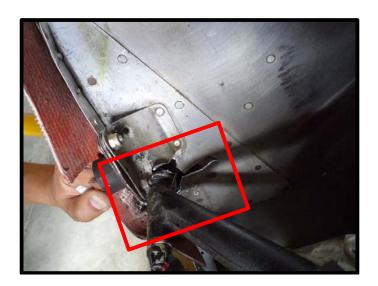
Vista del alternador de corriente, caído por la vibración.
